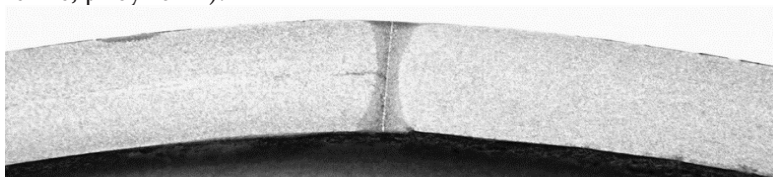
Сварка ТВЧ ТЭСЦ-3 сварное соединение без термообработки
